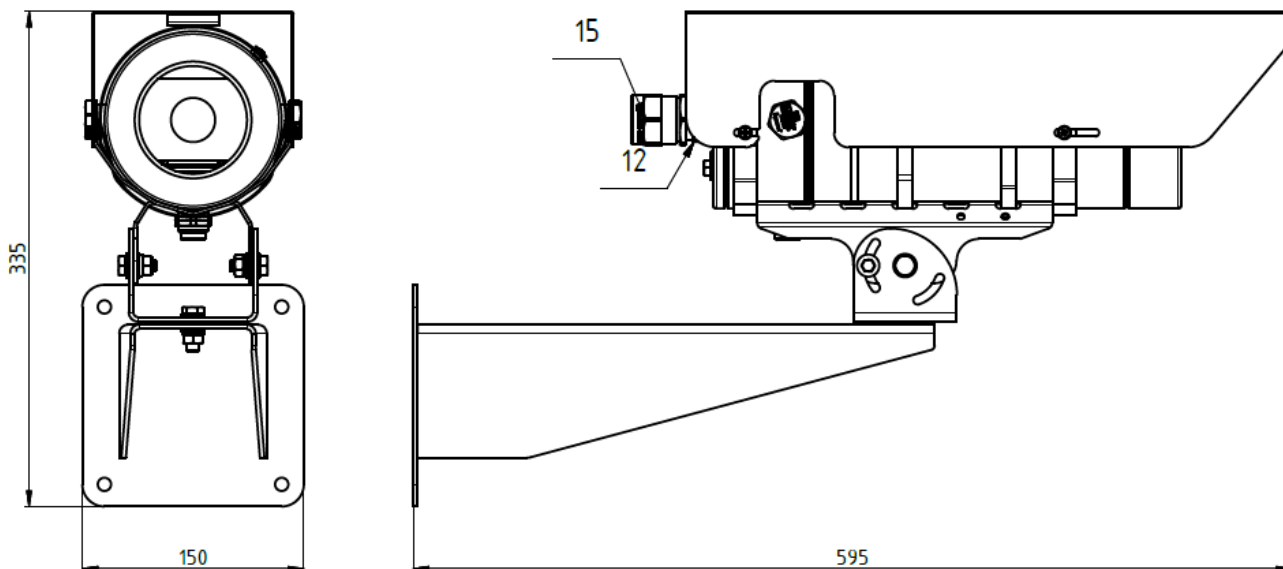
Габаритный чертеж видеокамеры ИВМС-501В.
